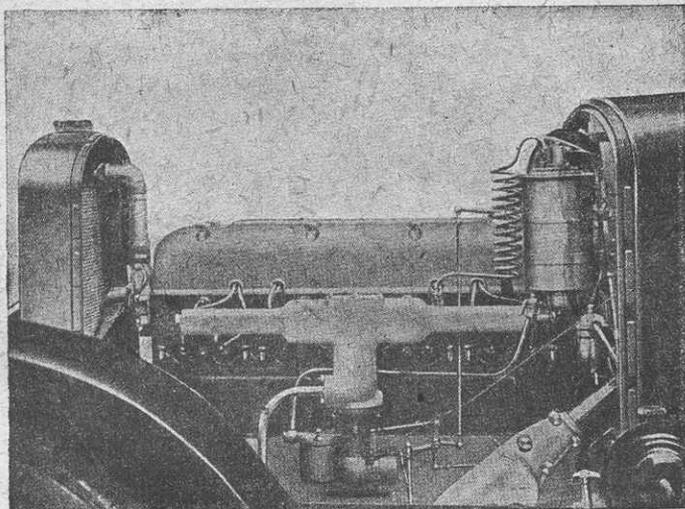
Восемьцилиндровый двигатель «Хорьх» (вид со стороны карбюратора).
